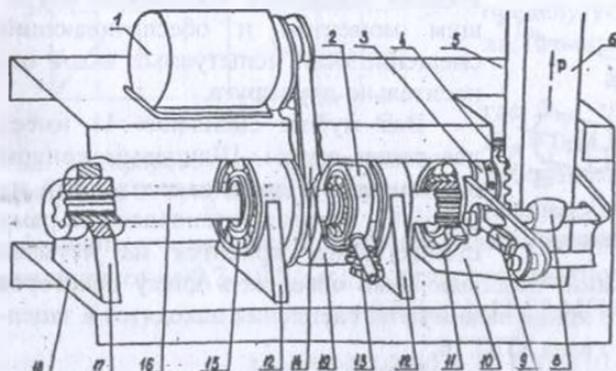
Стенд для испытаний шлицевых соединений (вала привода трактора Т-150 К): 1-электродвигатель; 2-подшипник эксцентрика; 3-шлицевой фланец; 4-зубчатая шестерня; 5, 18-рама стенда; 6-рейка; 7-ГРМ; 8-ролик; 9-сгонная муфта; 10-кронштейн; 11, 15-подшипник; 13-винт; 14-ремень; 16-испытуемый вал; 17-опора; 19-барабан.
